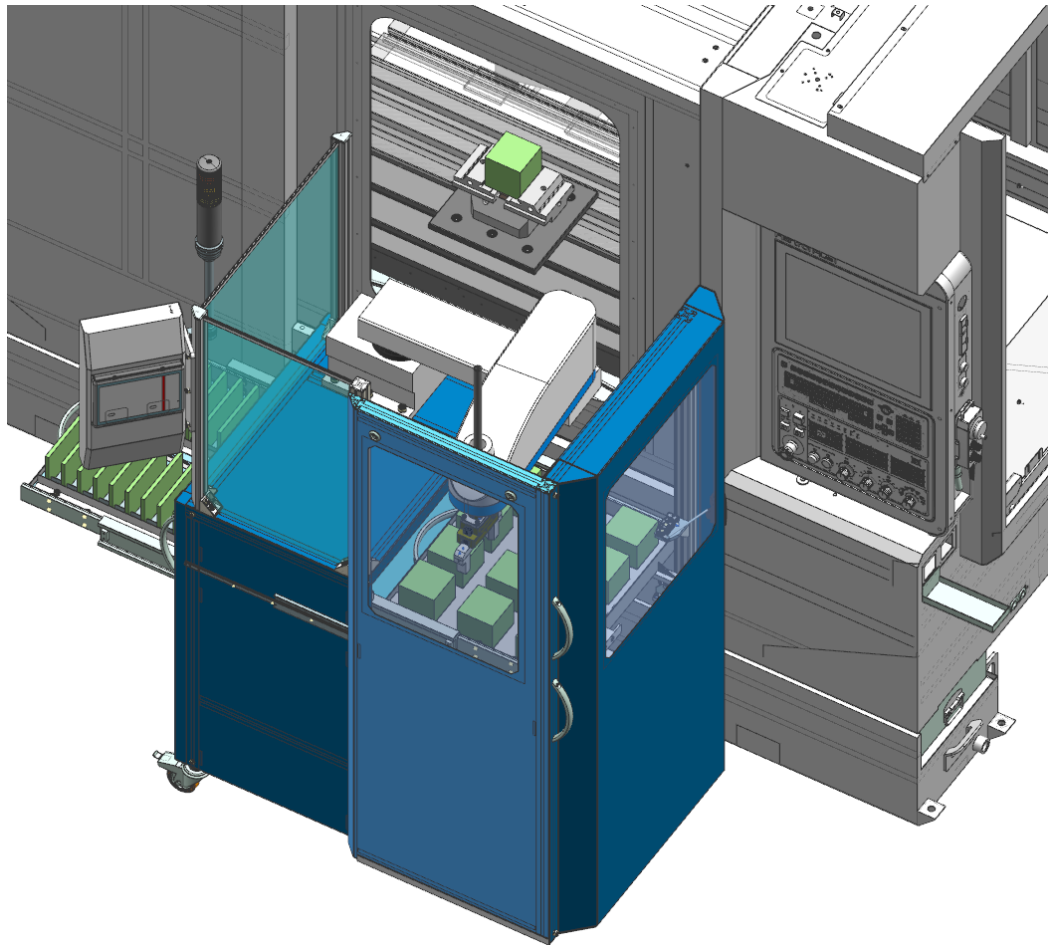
Zakládání polotovaru do svěráku - horní pohled
